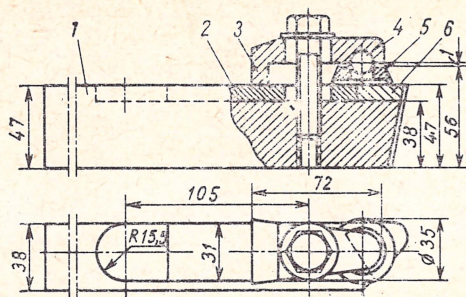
Стружко-ломатель к рез-цам колесотокар-ного станка
